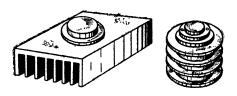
Конструкцин ребристых радиаторов для транзисторов.
